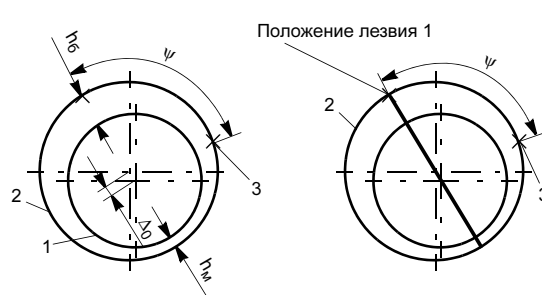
Схема установки инструмента: 1 — отверстие в заготовке; 2 — инструмент; 3 — метки на гильзе и шпинделе
